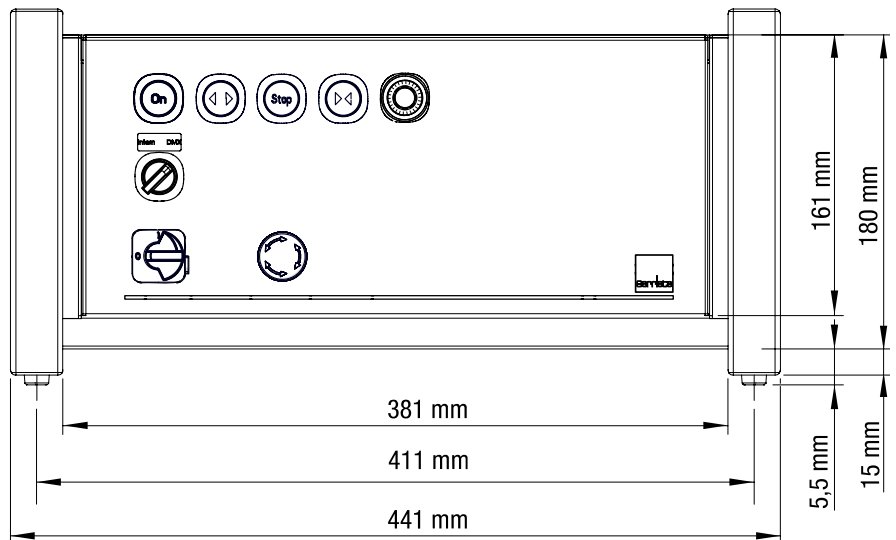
Frontansicht – Steuerung G-FRAME 54 (exemplarisch)
